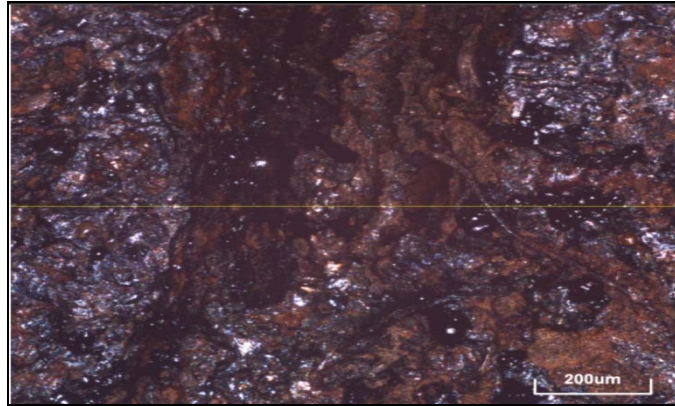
Área de fractura de la probeta con soldadura MMA.
